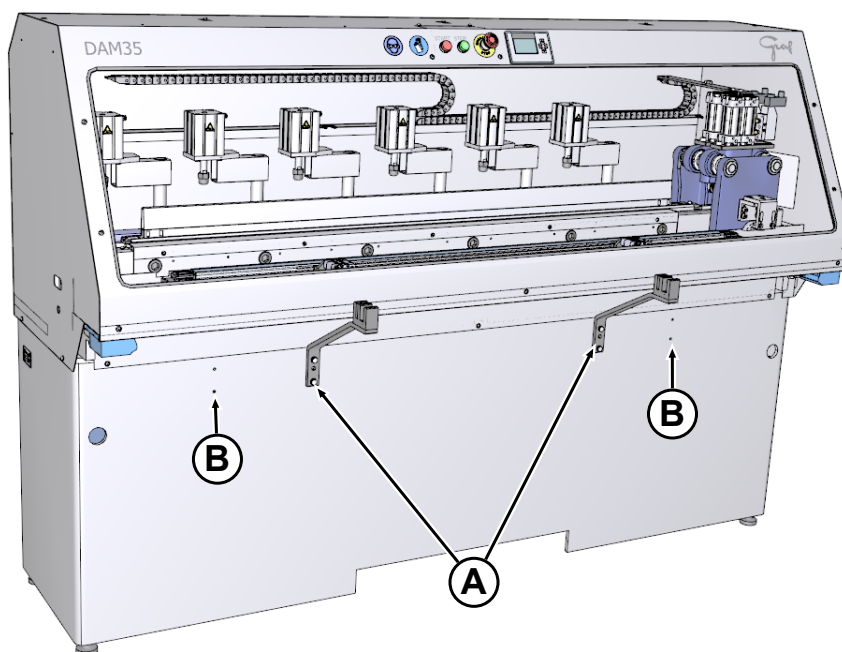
Posições possíveis dos suportes para o chapéu de cardagem
